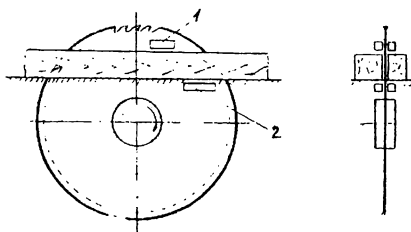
Установка пил на станке (схема установки направляющих диска):
